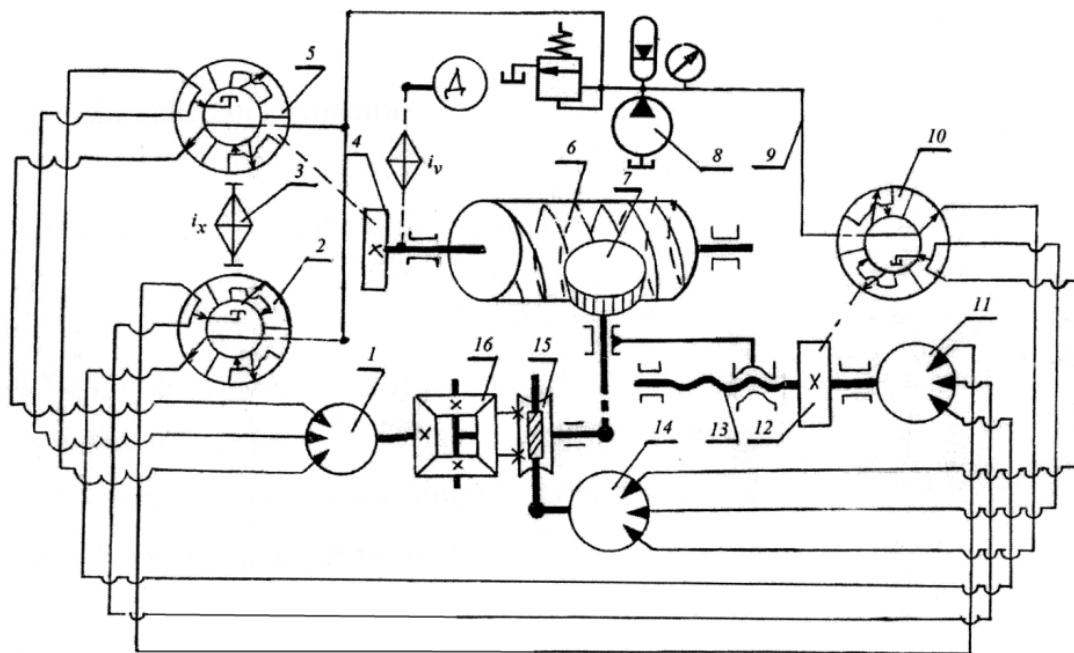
Структурная схема резьбонарезного станка с гидравлическими формообразующими связями для нарезания цилиндрических червяков обкатным резцом (долбяком)
